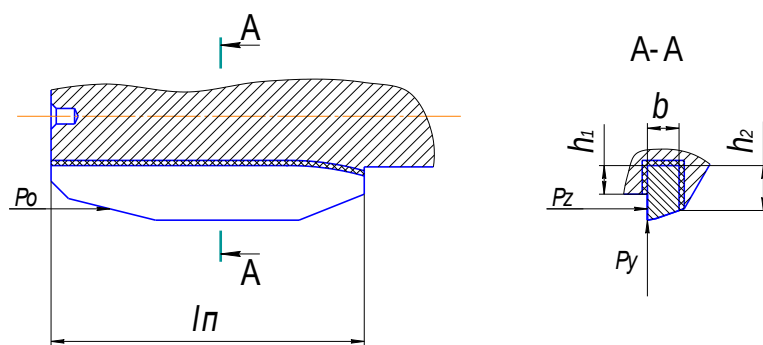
Соединение твердосплавной пластины с хвостовиком развертки
